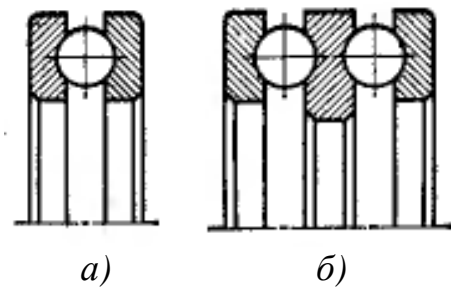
Шарикopідшипники упорні: а – одинарний серії 8000; б – подвійний серії 38000.
